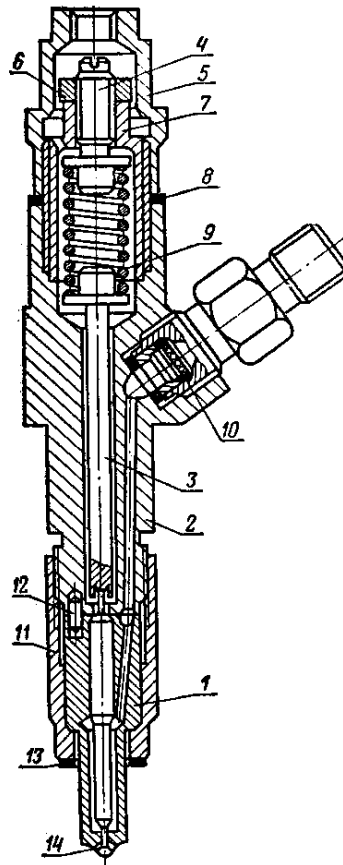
Форсунка: 1 — розпилювач; 2 — корпус форсунки; 3 — штанга; 4 — гвинт регулювальний; 5 — ковпак форсунки; 6 — контргайка; 7 — гайка регулювальна; 8 — прокладка; 9 — пружина; 10 — фільтр; 11 — гайка розпилювача; 12 — штифт установочний; 13 — прокладка форсунки; 14 — соплові отвори.
